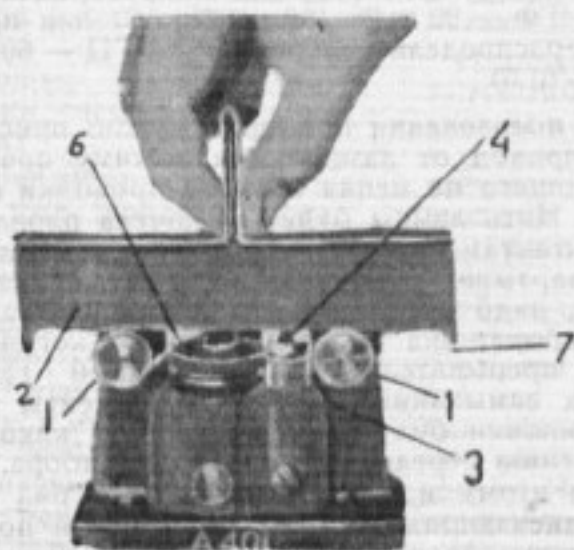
Шлифовка контактов прерывателя на специальном приспособлении
